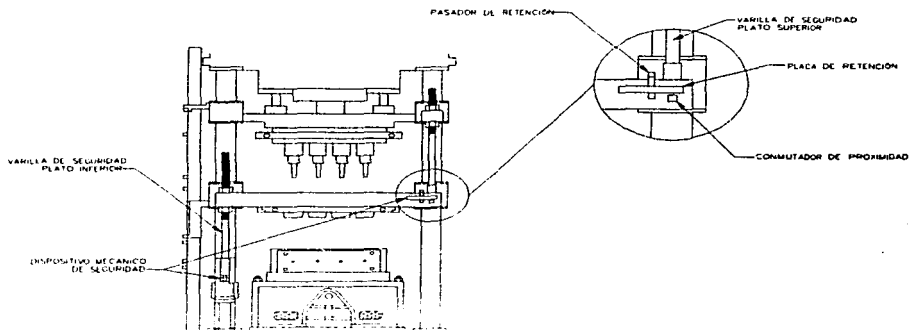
Dispositivo de seguridad para cierre de molde.
